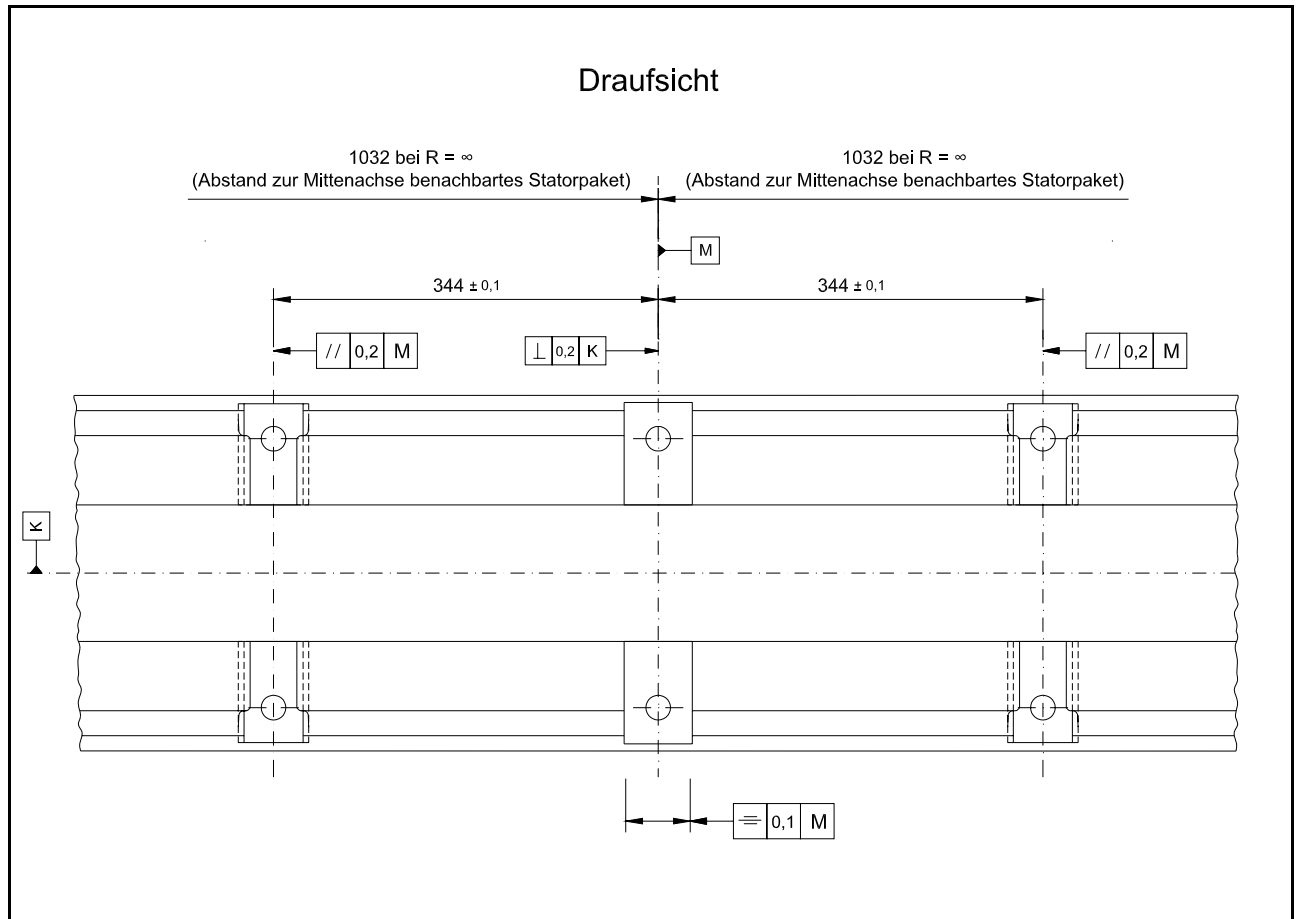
Maße und Toleranzen für die Ausführung der Statorpaketaufnahme in Stahlbauweise (Draufsicht)
